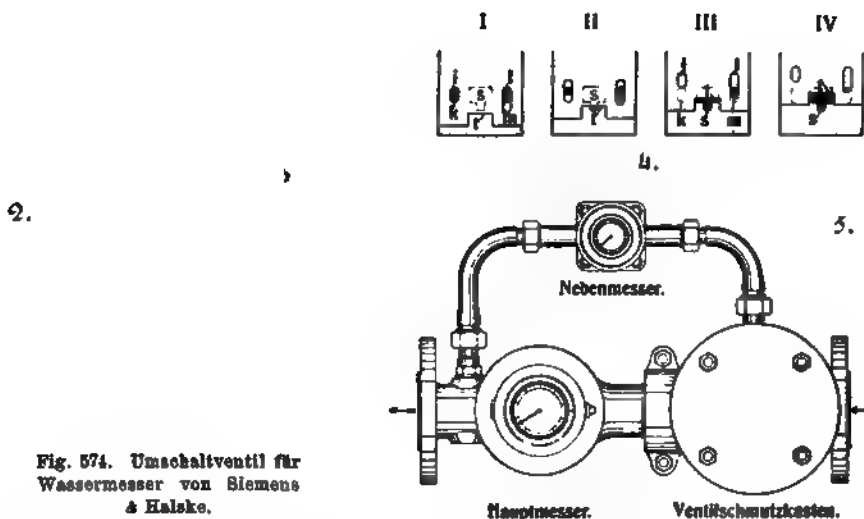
Umschaltventil für Wassermesser von Siemens & Halske.
